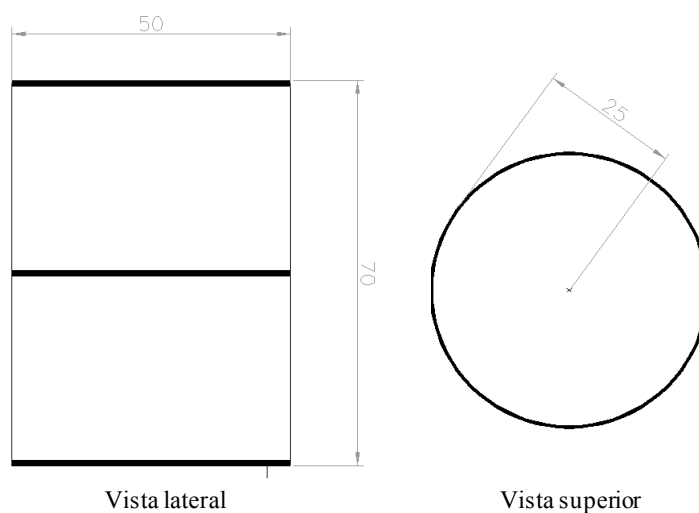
dimensões (em cm) do cilindro que compõe o corpo do silo, vista lateral e superior
